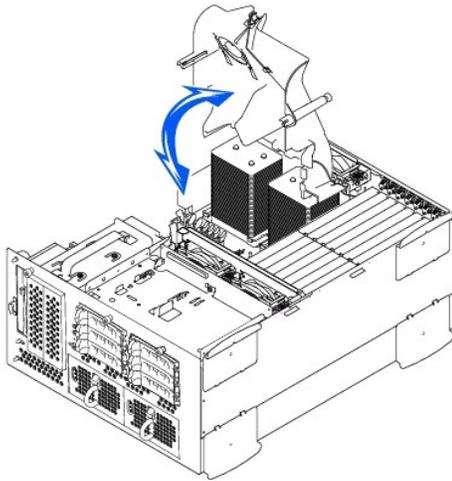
Kühlgehäuse entfernen und befestigen
